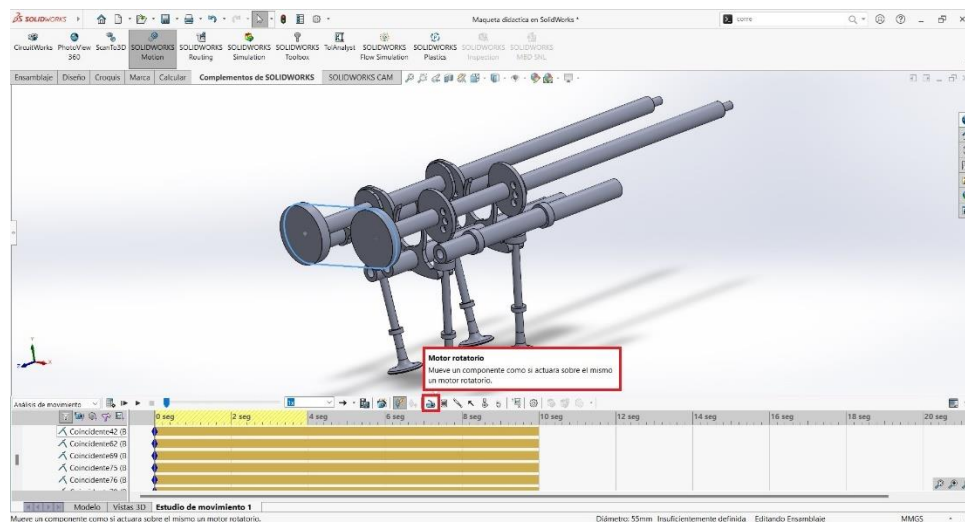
Motor de maqueta. Fuente: SolidWorks
